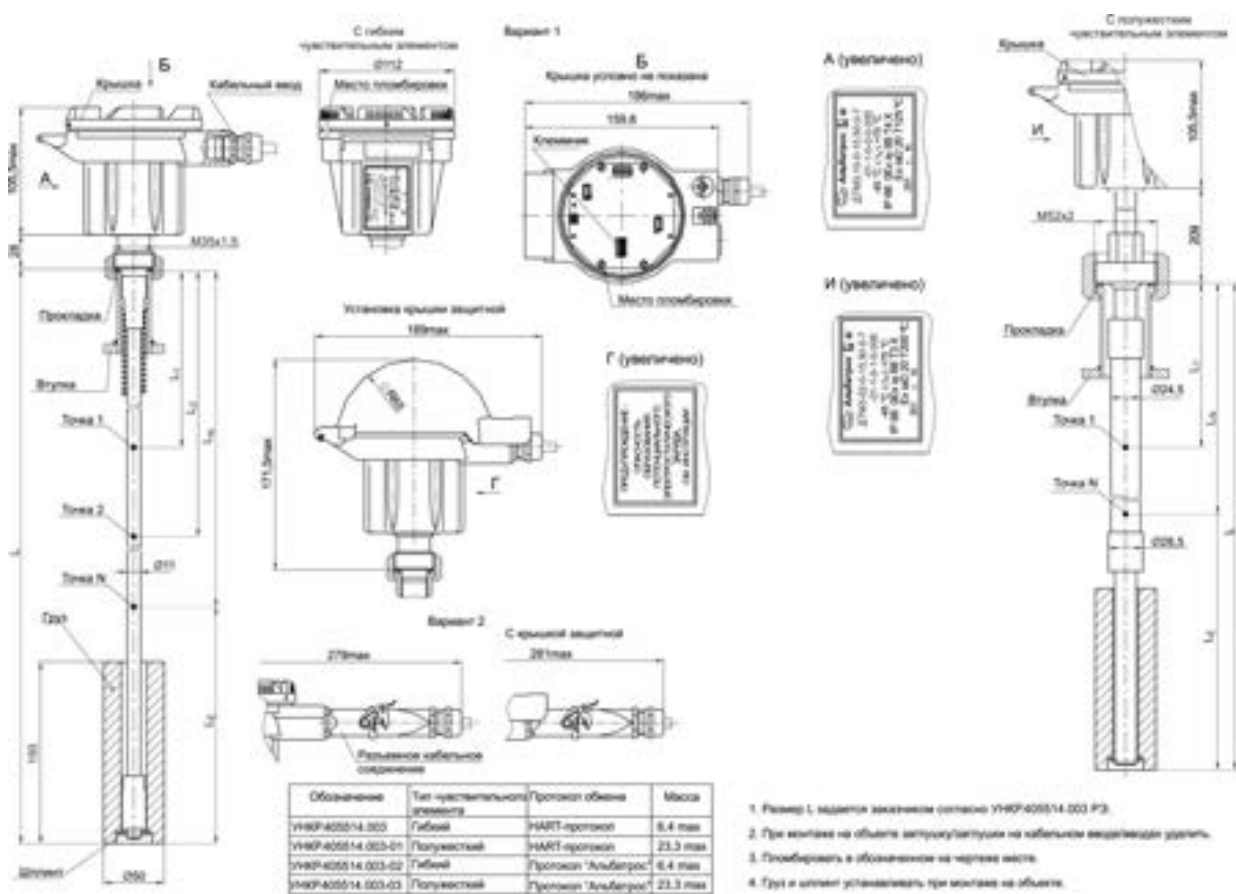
Габаритные размеры ДТМЗ
